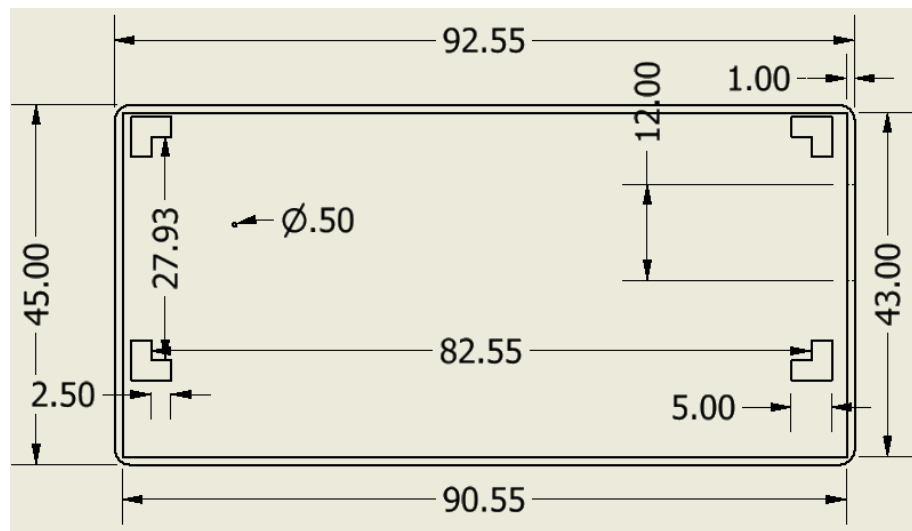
Planos caja uno, parte uno. (Fuente los autores).
